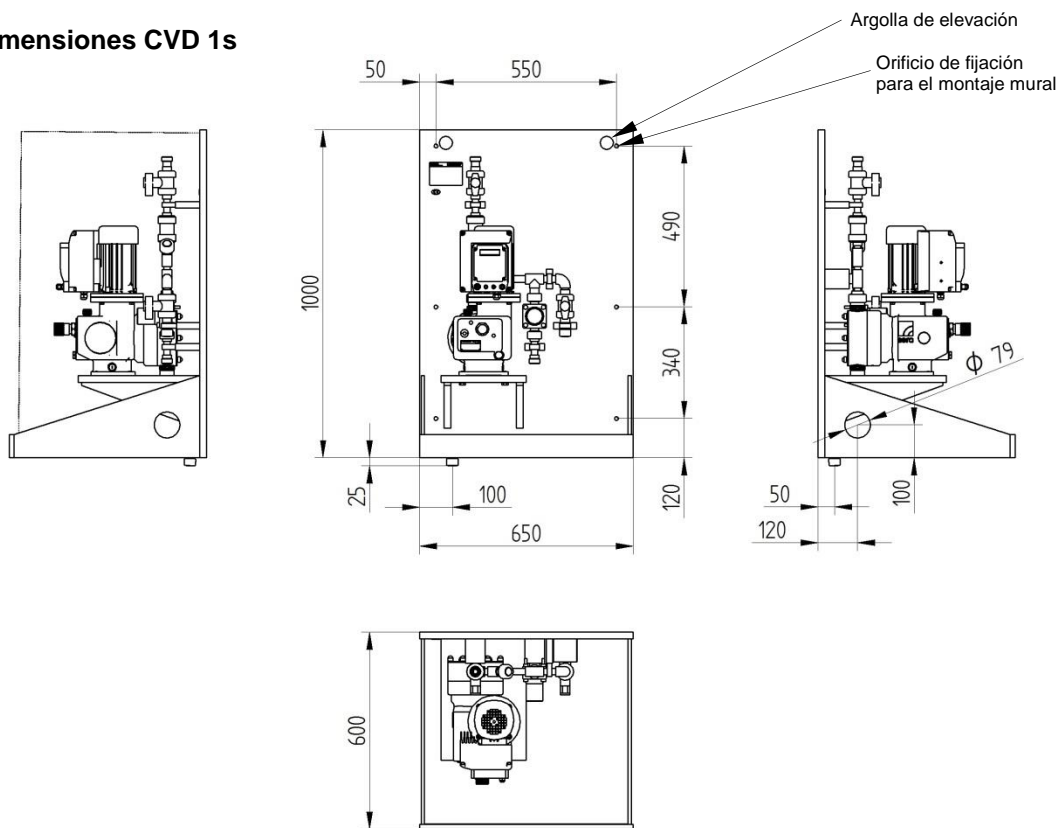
Dimensiones CVD1s (montaje en pared)
